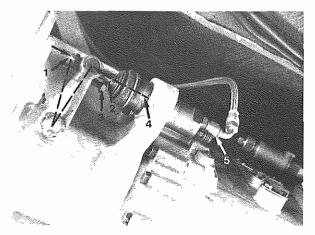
1) Dado - 2) Puntalino - 3) Vite - 4) Anello seeger - 5) Tubo 1) Nut - 2) Adjusting rod - 3) Screw - 4) Retaining ring - 5) Tube
